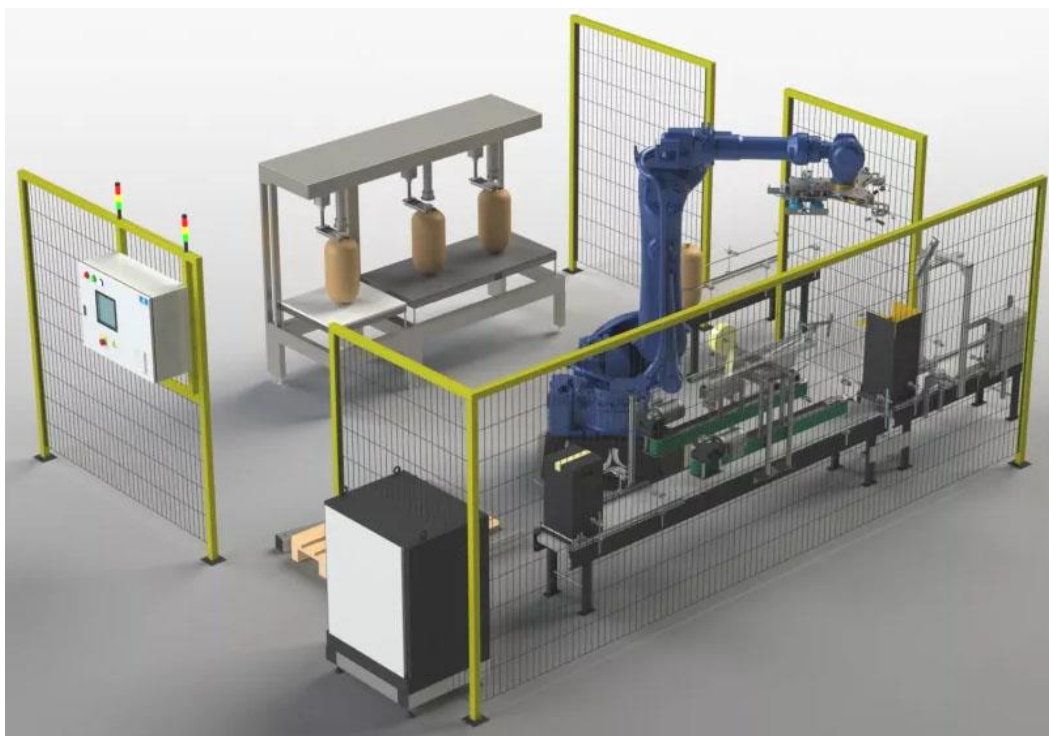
Общий вид мехатронного участка розлива напитков и упаковки в короба
